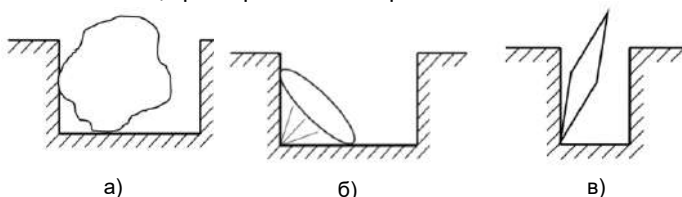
Расположение наполнителя для обработки сложных участков поверхности деталей: а – абразивное зерно; б – зерно в виде конуса; в – игла
